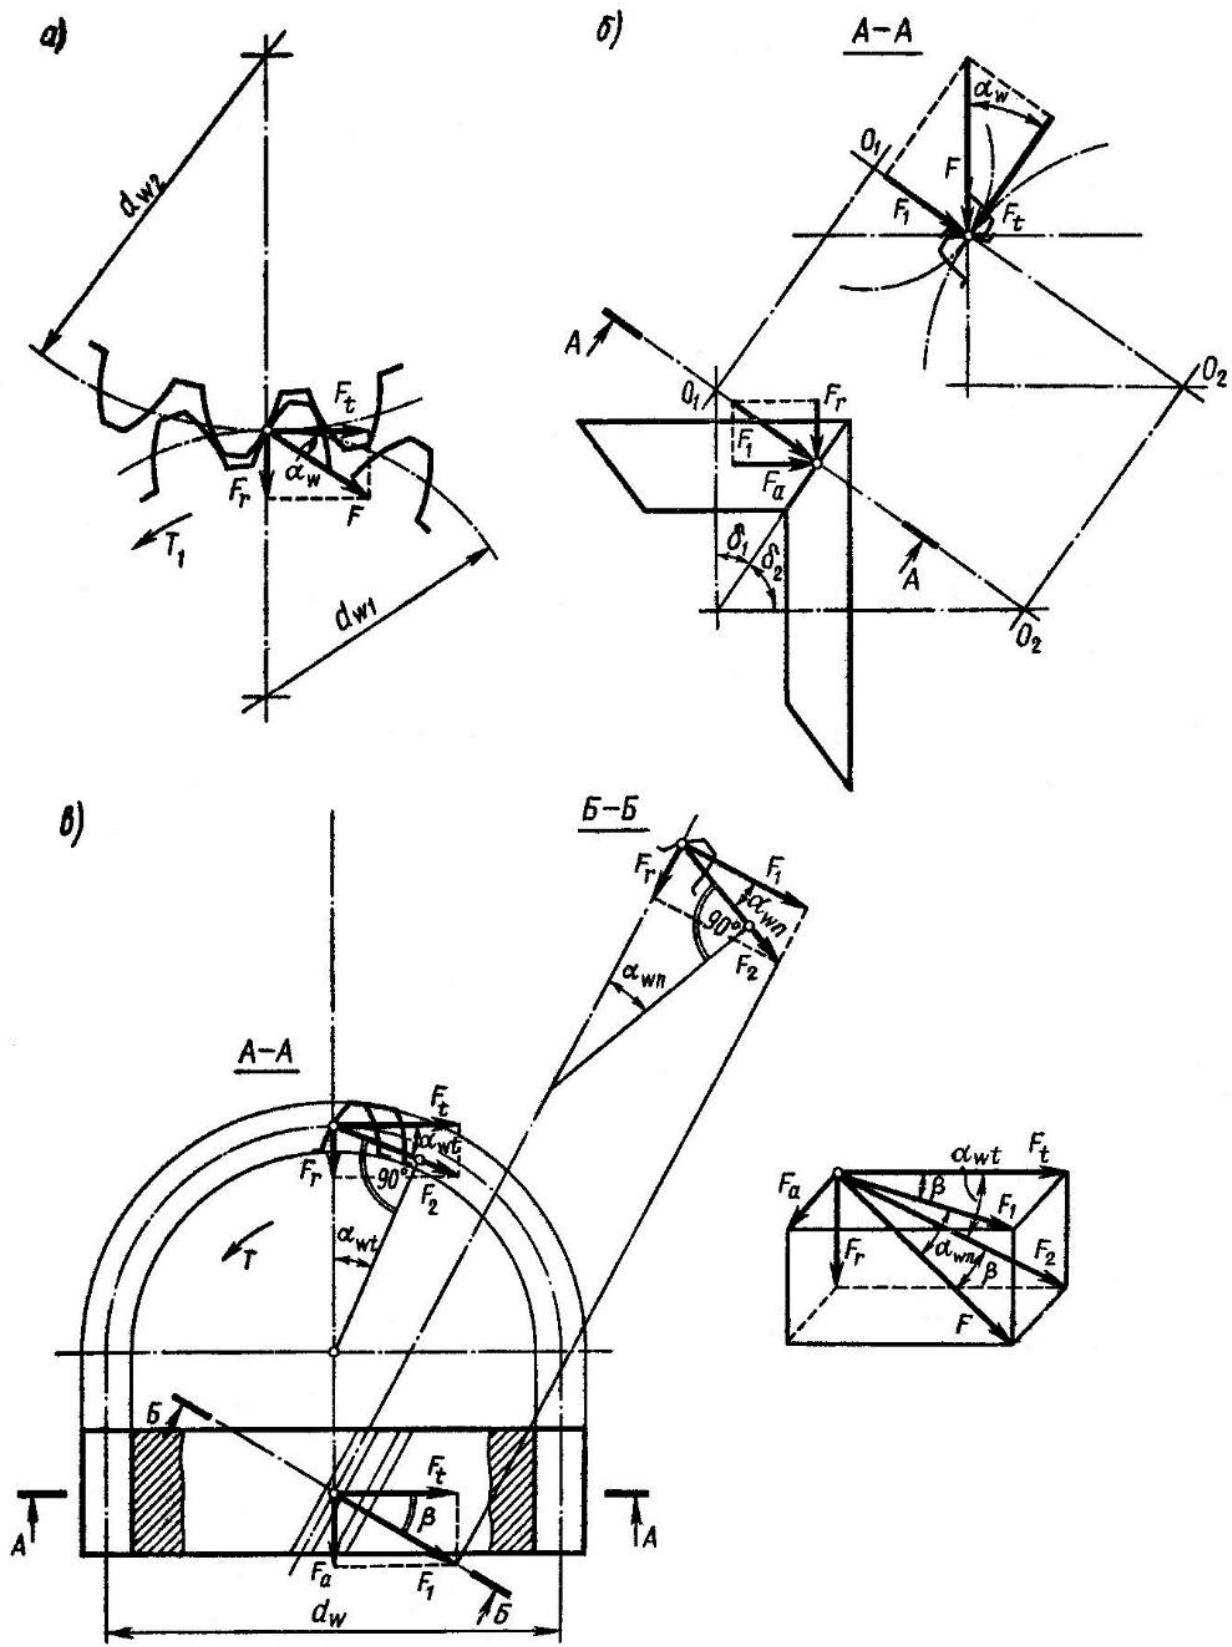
Схемы сил, действующих в зацеплении зубчатых передач
